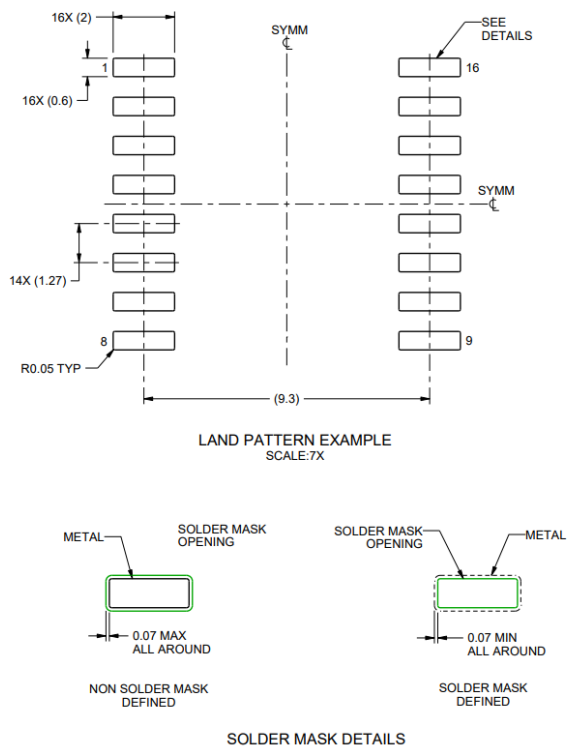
Croquis perfiles soldadura de PCF8574APWR.
